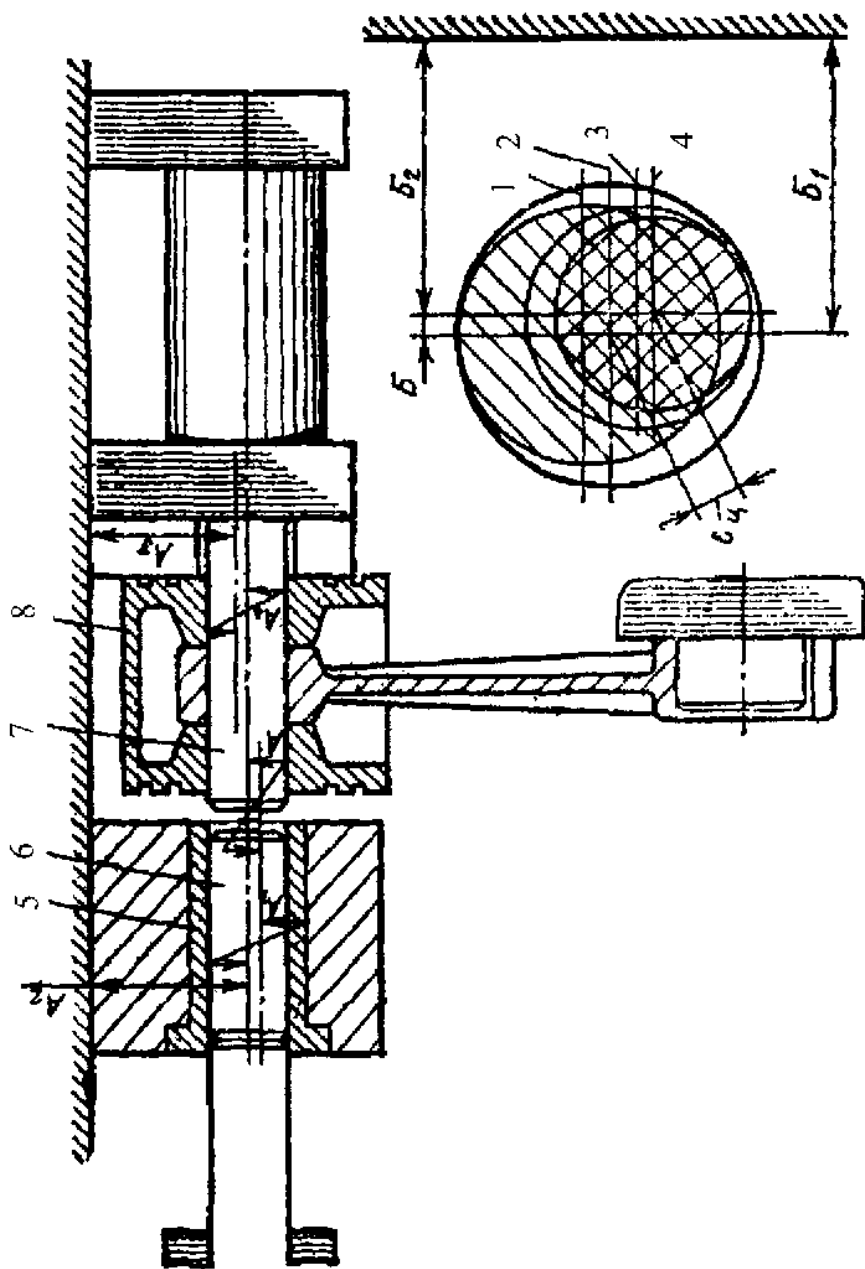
Схема базування при складанні поршня з пальцем і шатуном:
